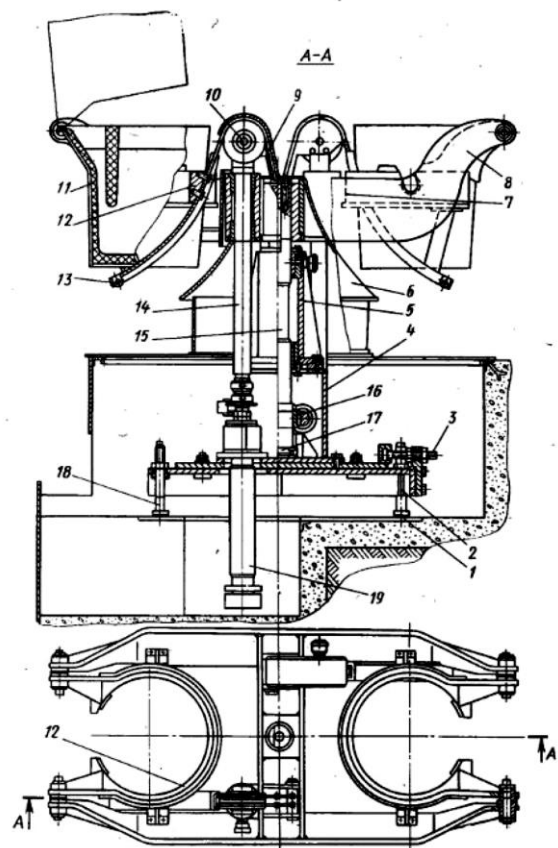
Конструктивна схема двопозиційного залівального автомату
